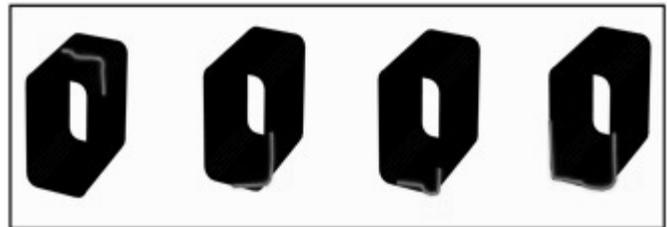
Configuración de grietas en L y U sobre componente rectangular
